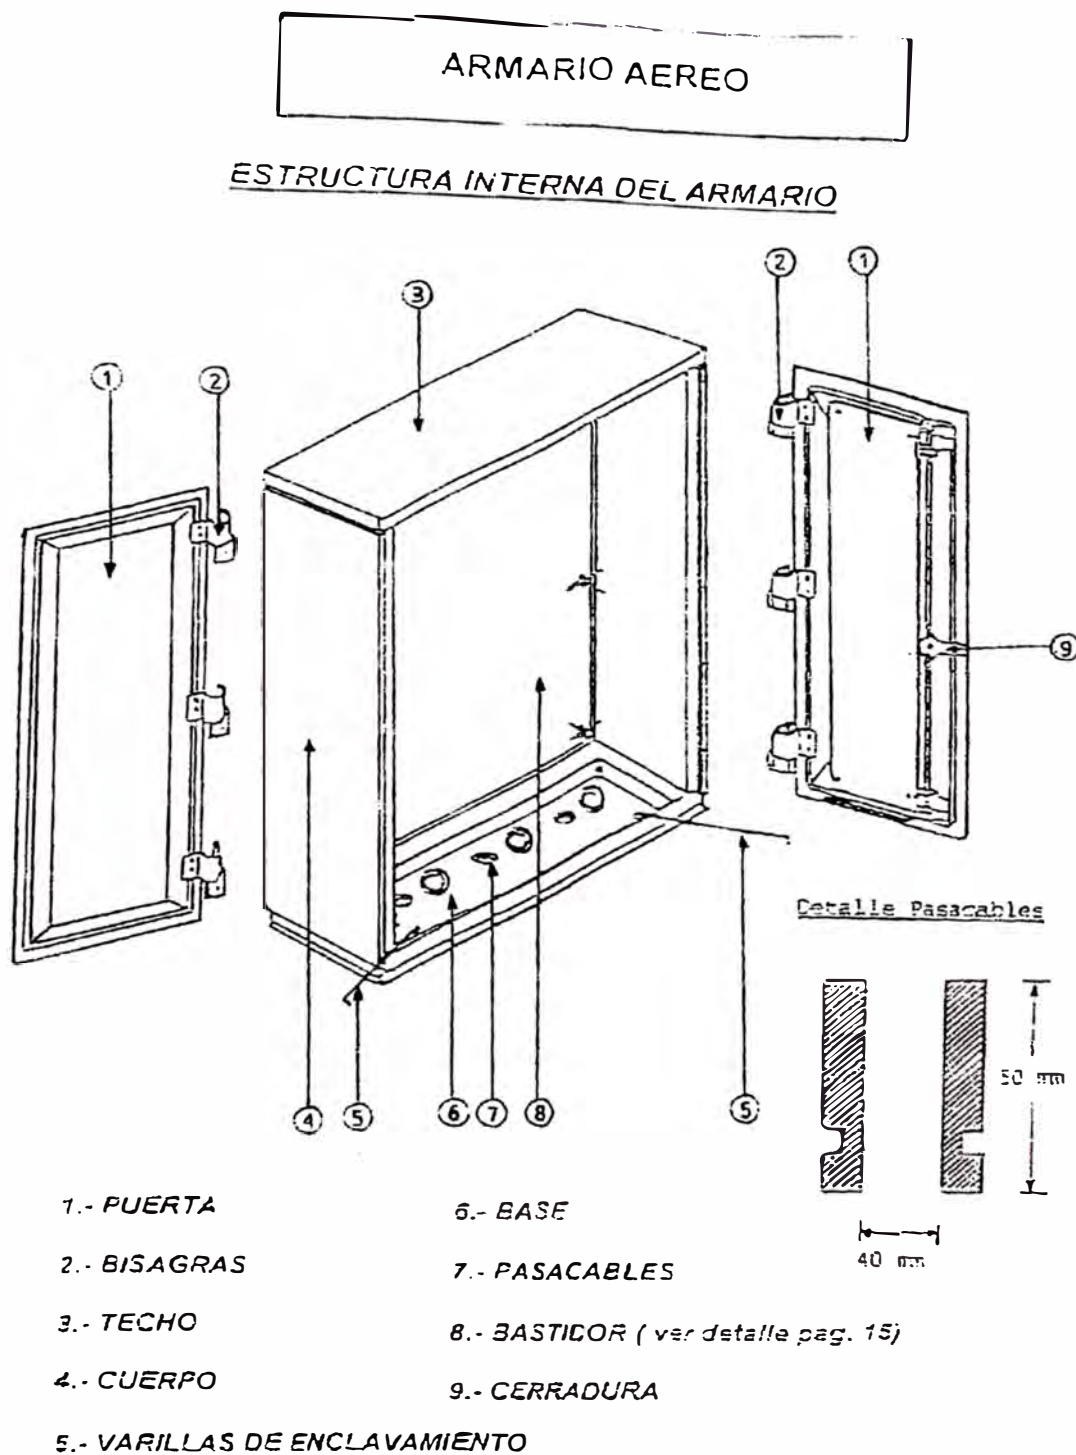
ESTRUCTURA INTERNA DEL ARMARIO
